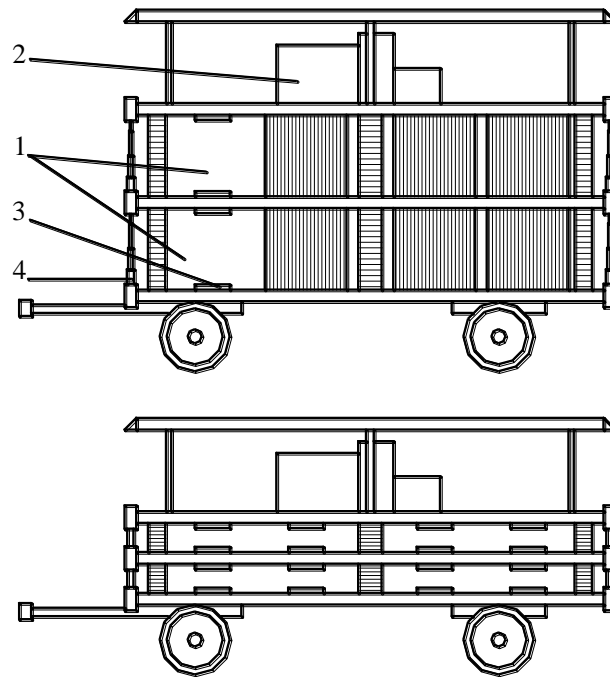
Пересувна двоярусна сушарка для паковок різної форми: 1 – вентиляційна камера; 2 – повітрорудовно-нагрівальний пристрій; 3 – отвір; 4 – телескопічний блок
